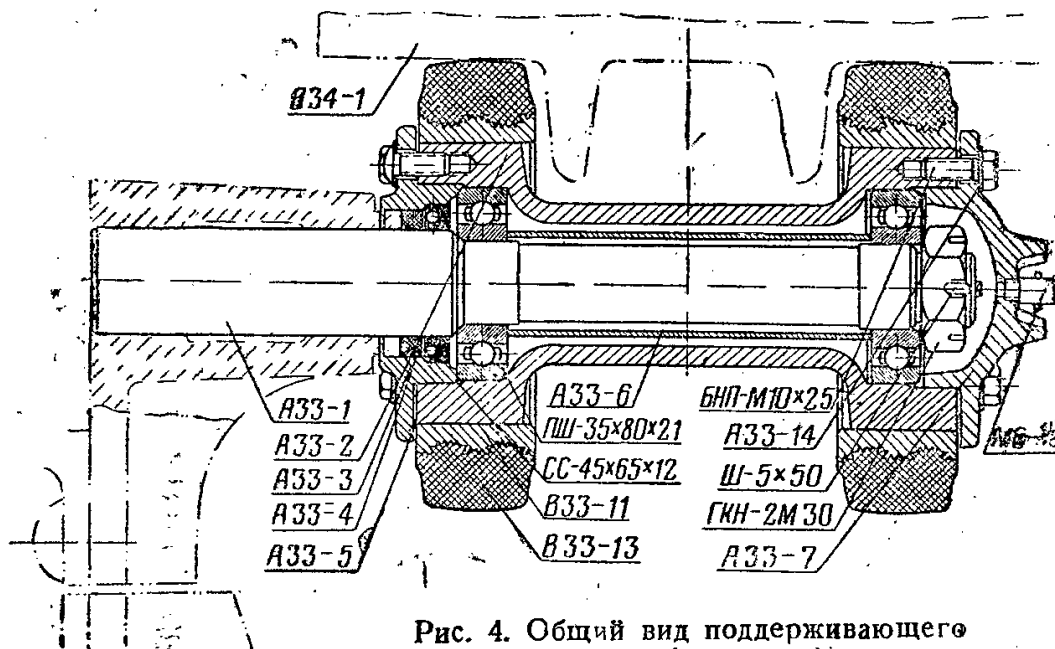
Общий вид поддерживающего ролика (в разрезе)
